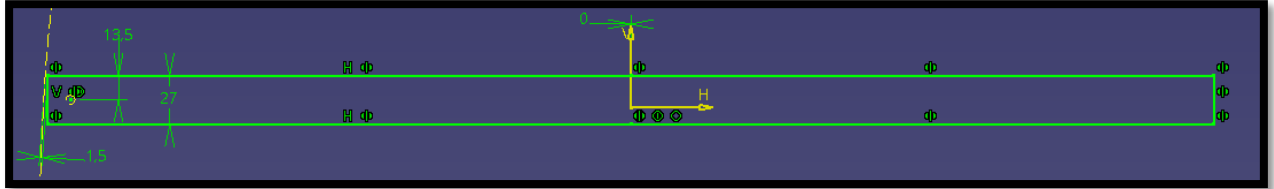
Barra horizontal 11: Sketch correspondiente
